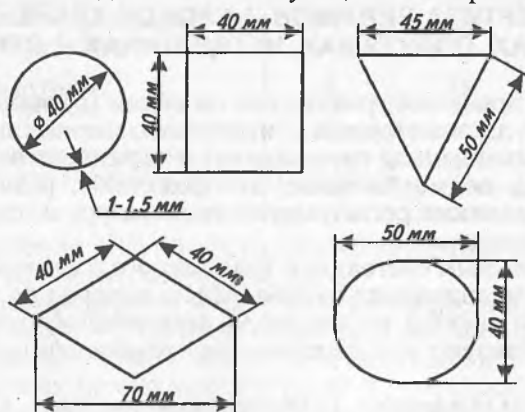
Формы и размеры клейм для товароведческой маркировки мяса
